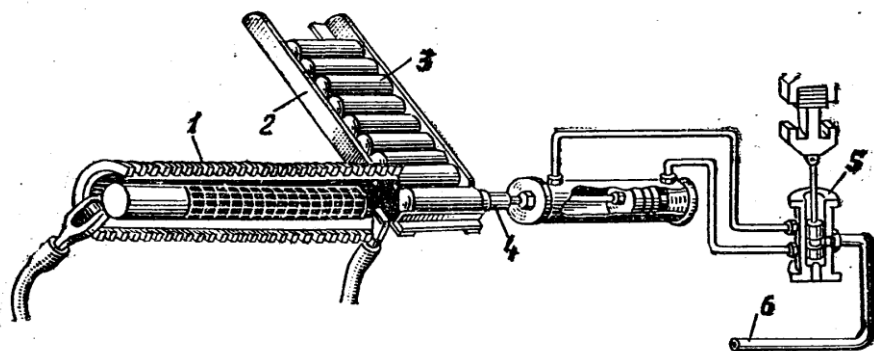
Схема индукционной нагревательной установки непрерывного действия
